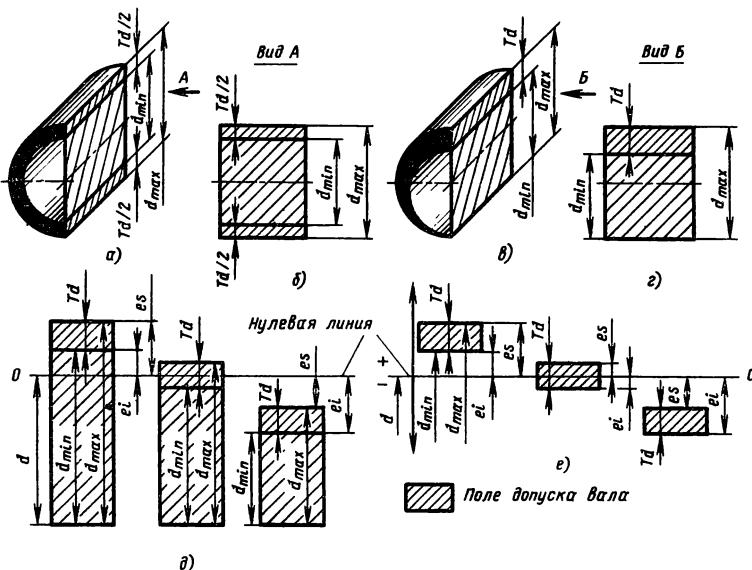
Симметричное (а и б) и одностороннее (в и г) распределение допуска вала; варианты расположения поля допуска вала относительно нулевой линии (д), принятая схема изображения полей допусков (е)
